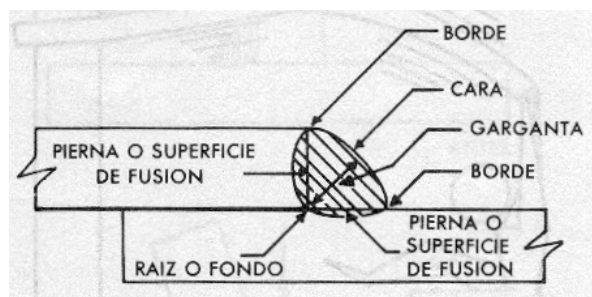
Términos comunes aplicados a una soldadura.
